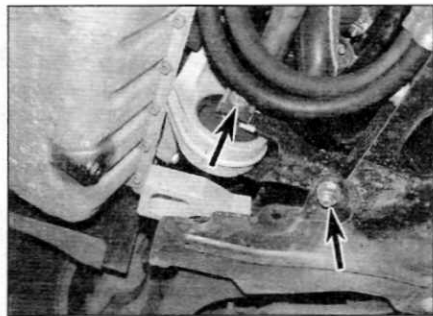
Болты/гайки крепления стяжки задней опоры двигателя/коробки передач (отмечены стрелками)
